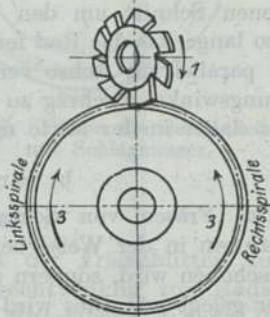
und 613. Fräsen der Schraubenträder nach dem Teilverfahren.
